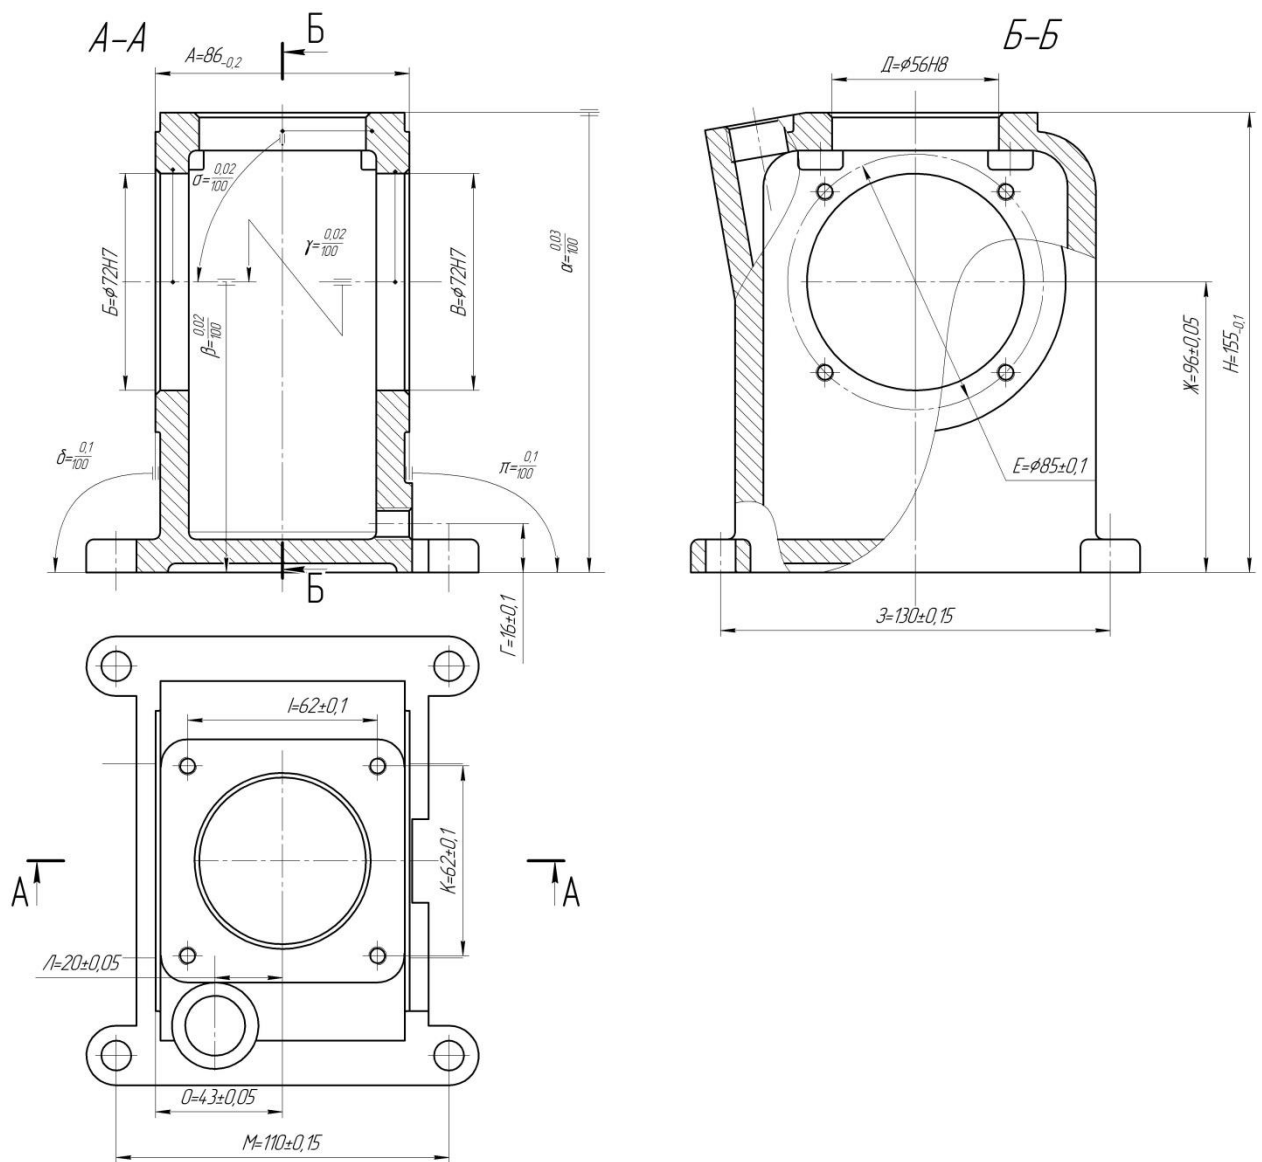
Розмірні зв'язки корпусу, які необхідно вирішити під час механічної обробки корпусу вакуум-насосу
